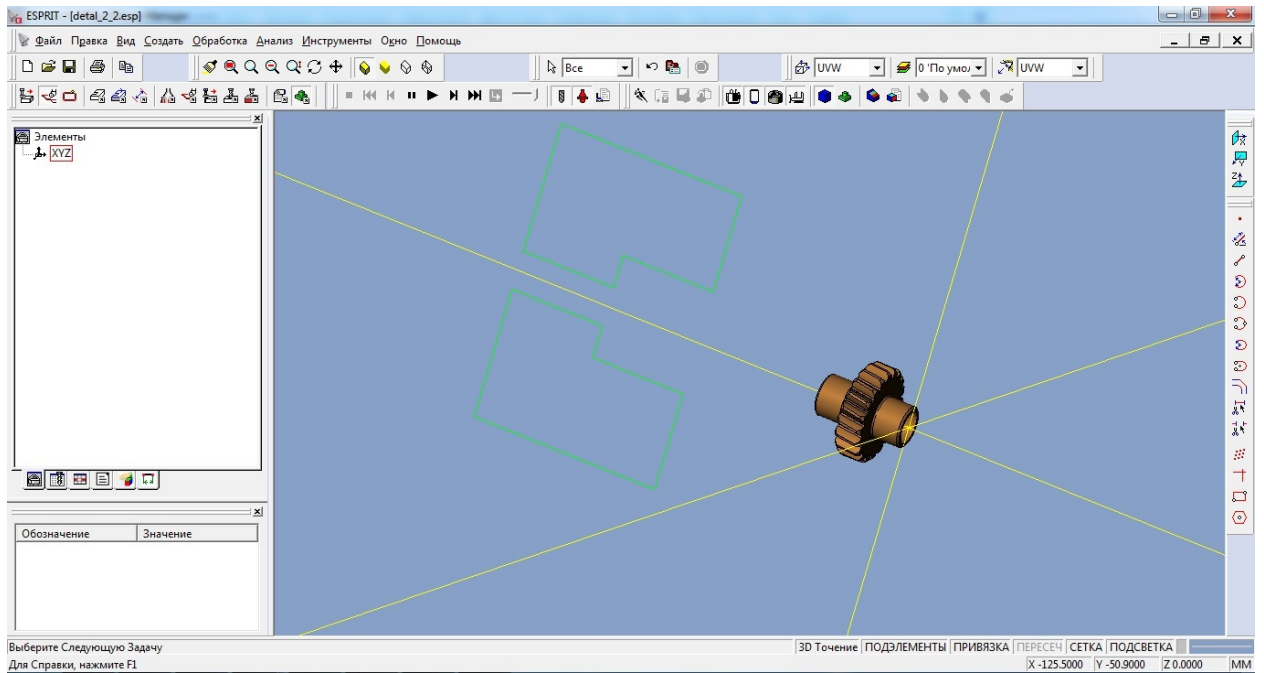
3D модель вала-шестерни у середовищі Esprit
